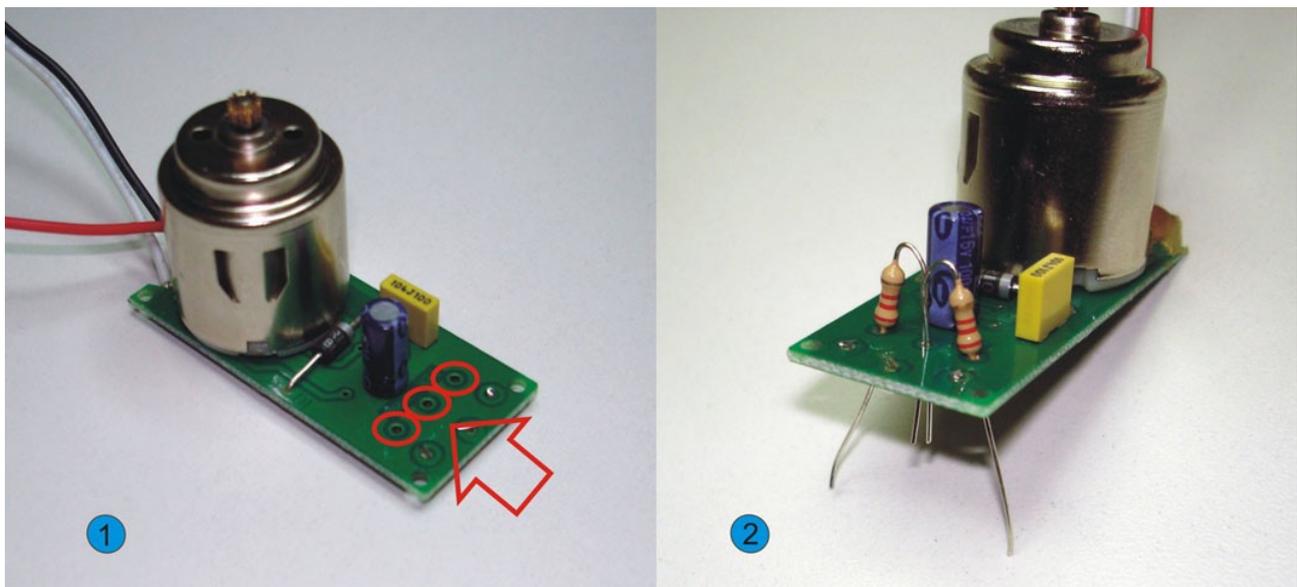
Soldagem dos resistores. 1-Placa de controle com destaque para o local a soldar os resistores. 2-Resistores na placa.
